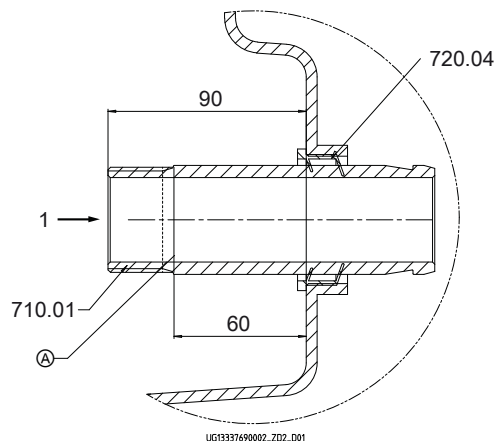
Druckrohr montieren und Einbaumaß einstellen, Abmessungen [mm]
